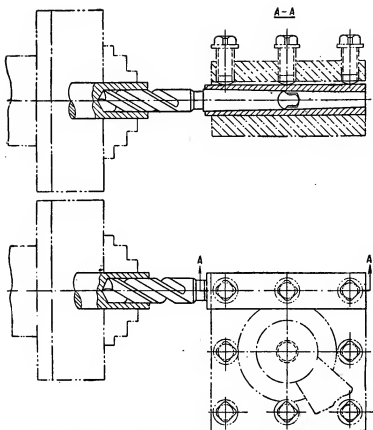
Установка сверла в специальной втулке, укрепленной в резцедержателе токарного станка.
